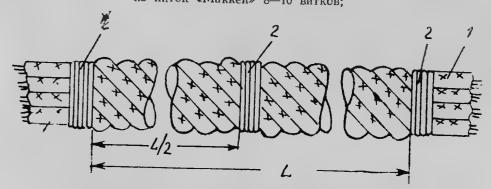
Скручивание проводов электрожгута: 1 — провод; 2 — бандаж из ниток
